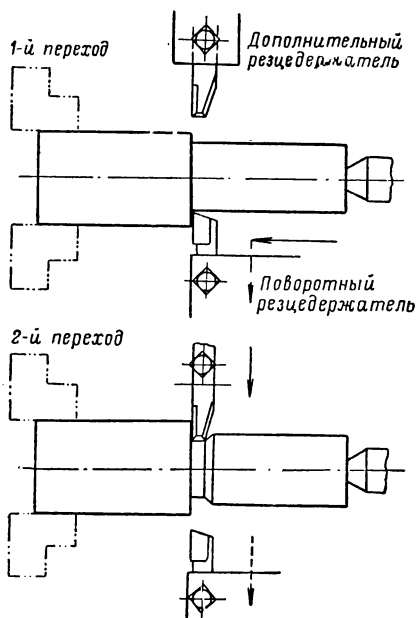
Обработка ступенчатого валика с помощью дополнительного заднего резцедержателя.
